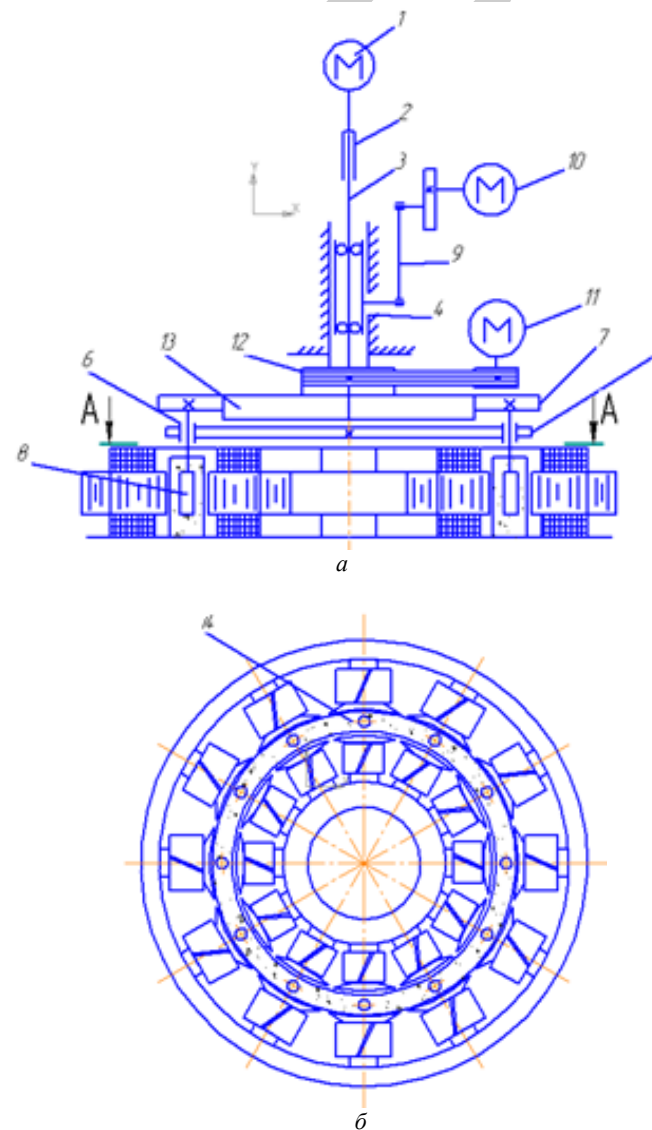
Схема установки для МАО поверхностей деталей машин типа «кольцевая ванна»: а – кинематическая схема установки; б – «кольцевая ванна»
